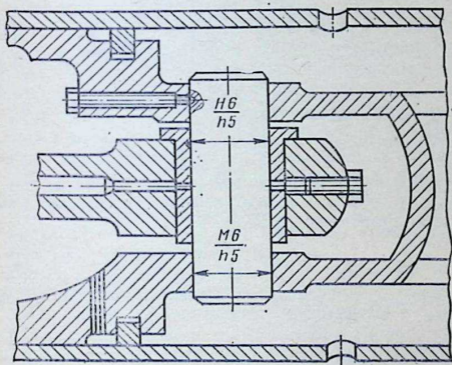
Пример применения системы вала (сопряжение поршень — палец — втулка верхней головки шатуна компрессора).
